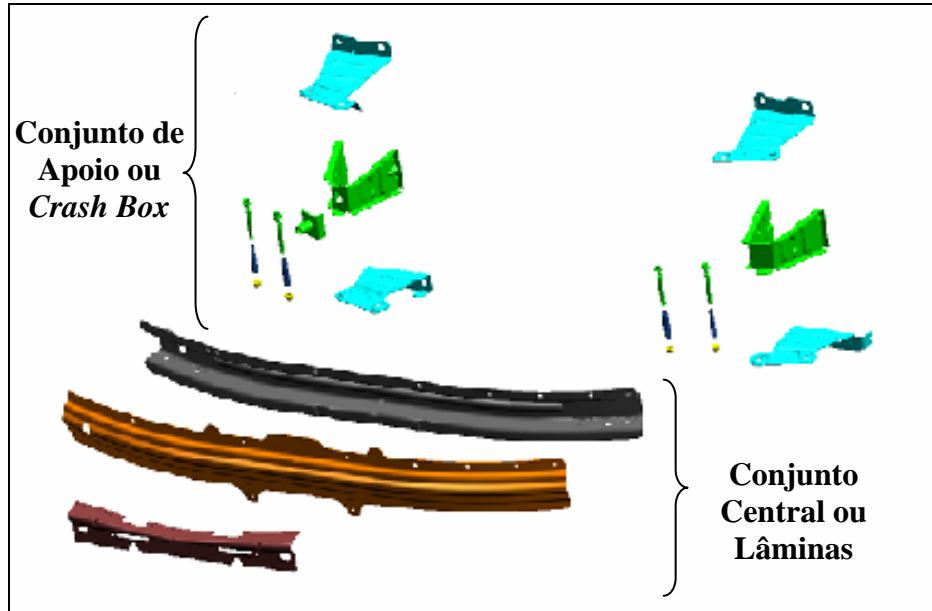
Subconjunto de peças a serem soldadas.
